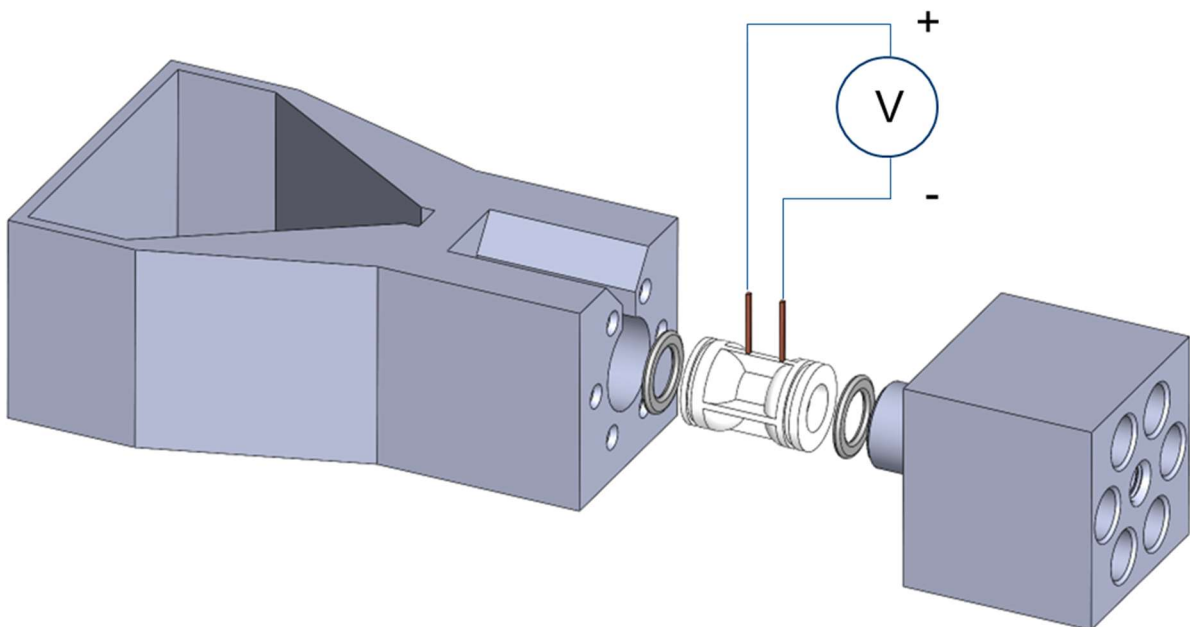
CAD Zeichnung des Halters für die weiß dargestellte elektroosmotische Pumpe.
